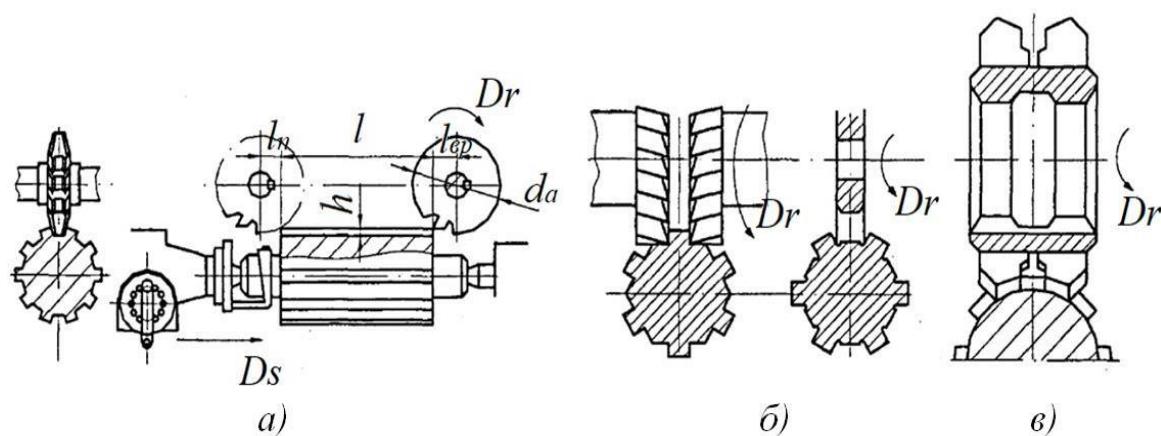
Способи фрезерування шліців дисковими фрезами [24]
